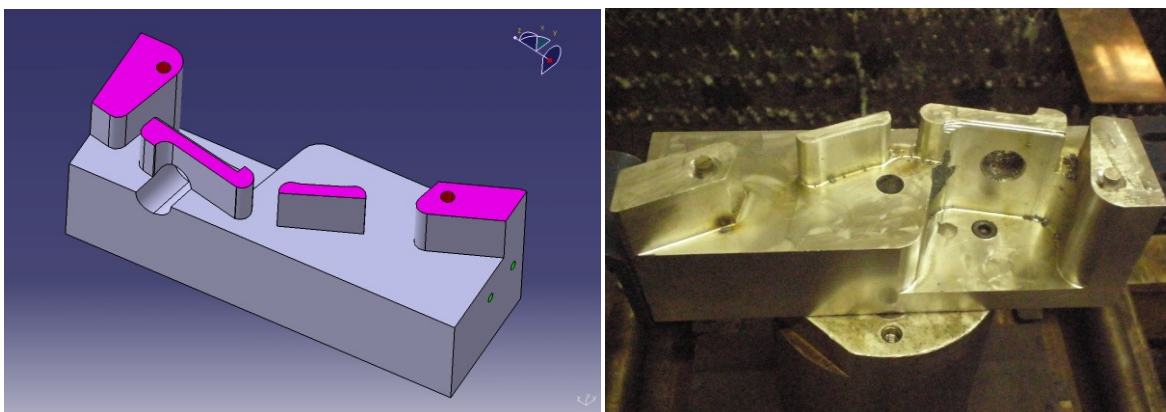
Gabarit de Corte Laser ‘Filler Head Bracket’ – Modelação/Ferramenta
